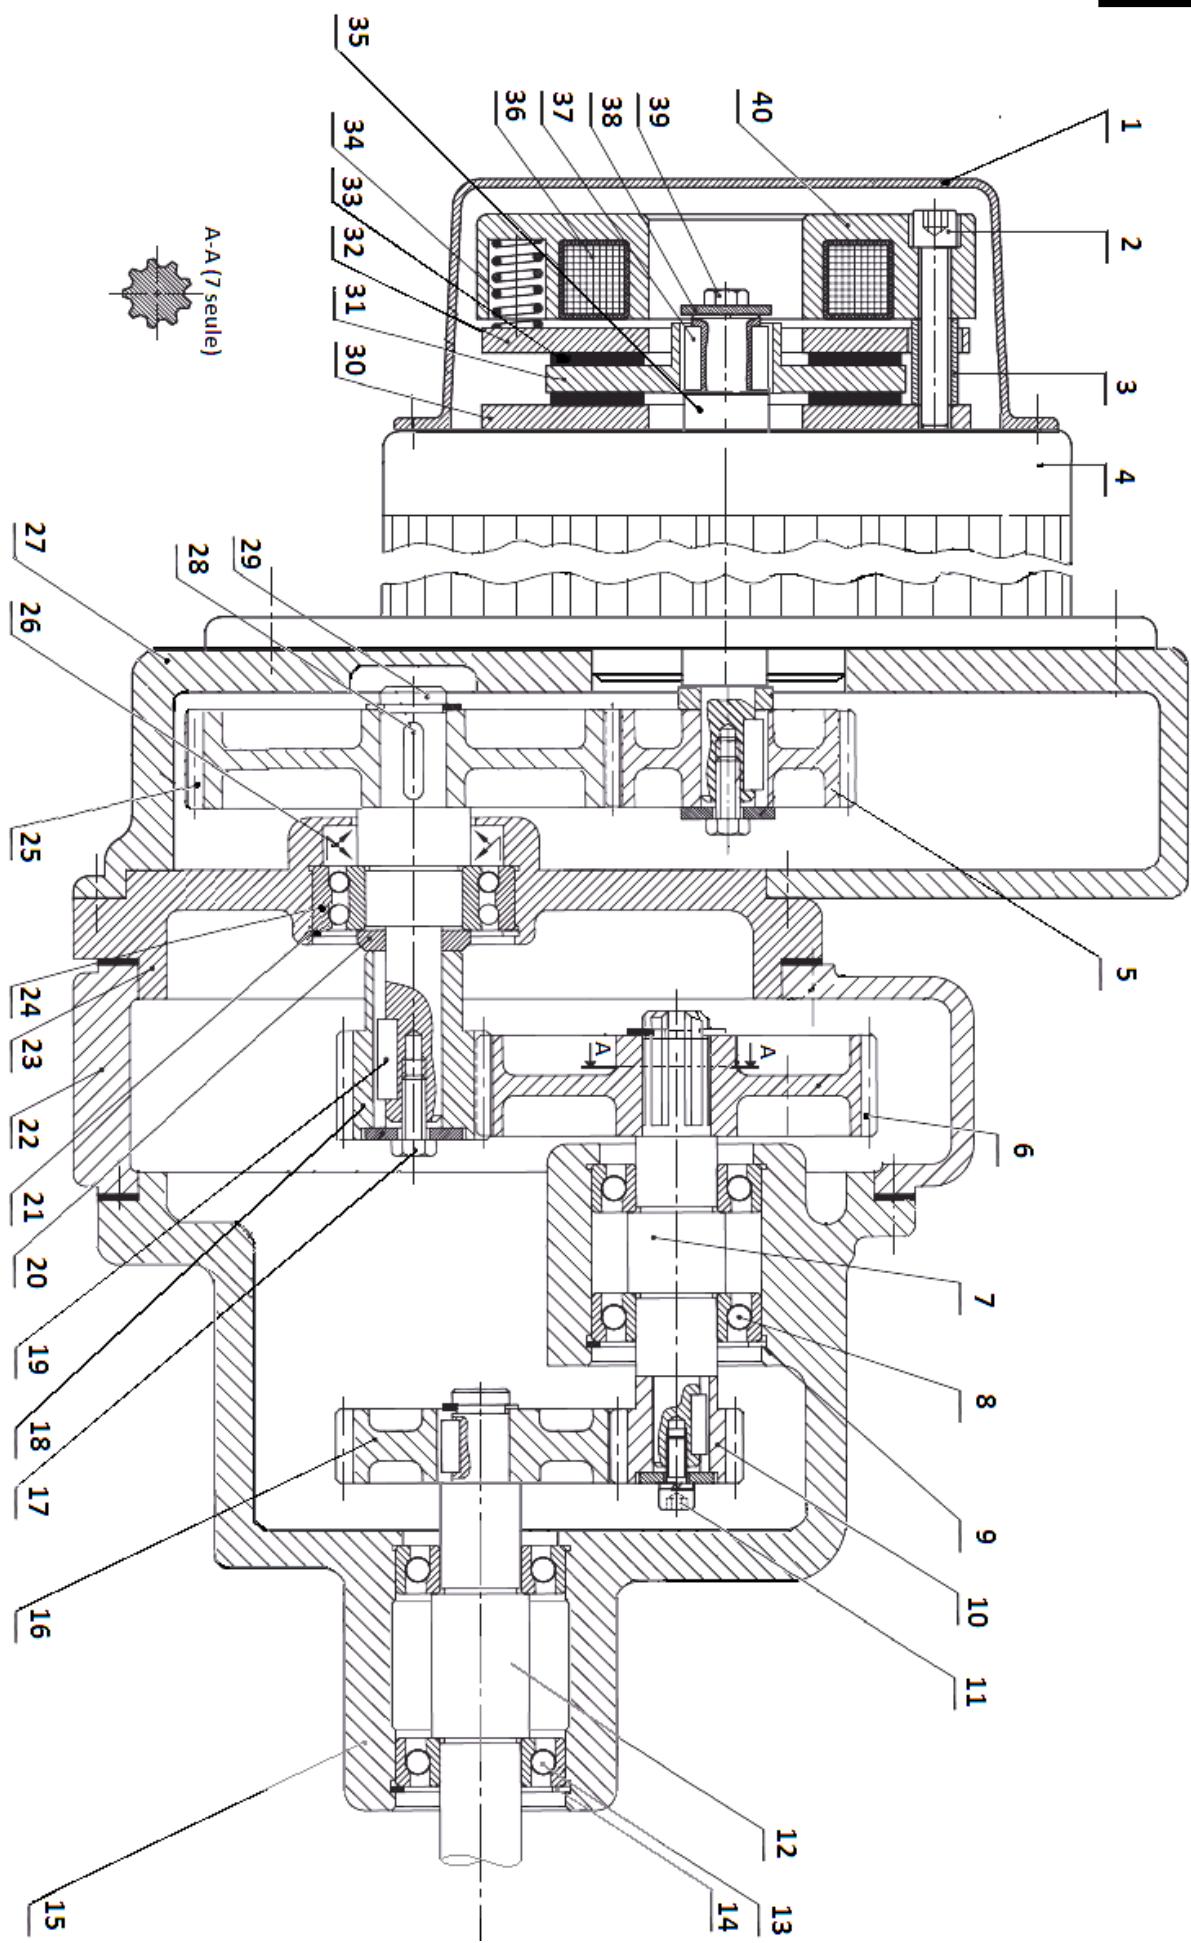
Dessin d'ensemble du moto-réducteur-frein
